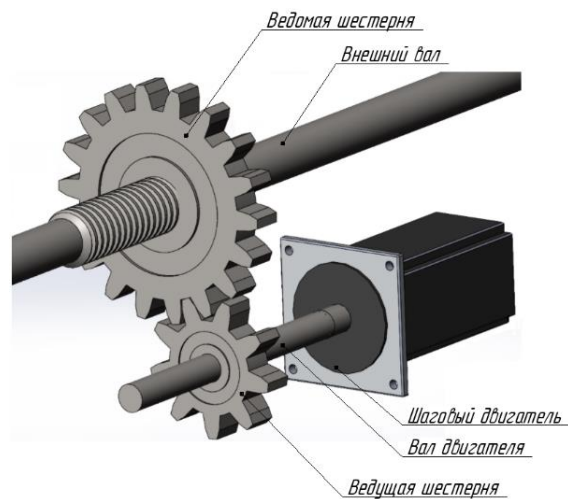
Общий вид механизма для передачи возвратно-поступательного движения
